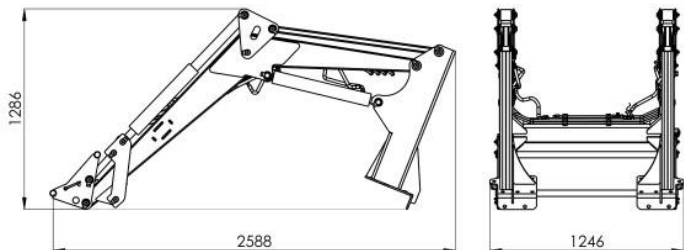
Размеры погрузчика, подготовленного для транспортировки как груз.
